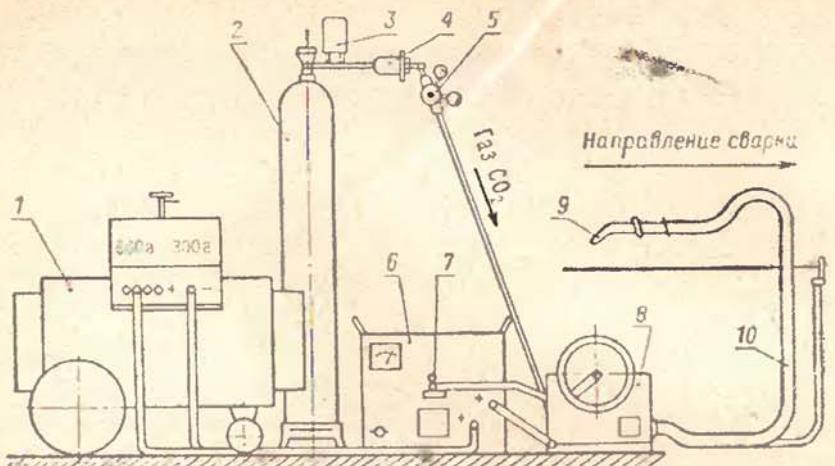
Общая схема установки для полуавтоматической сварки в среде защитного газа плавящимся электродом:
